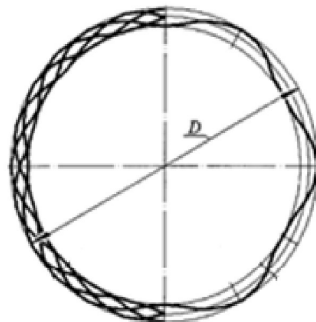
Поперечный разрез заготовки после обработки поверхности вибронакатыванием со статико-импульсным нагружением
